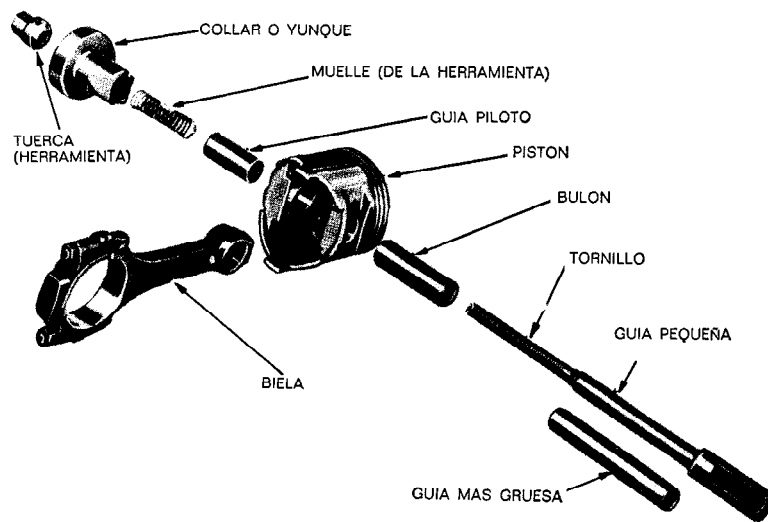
Disposición de la herramienta para montar un bulón (Chrysler-Plymouth of Chrysler Motors Corporation).
